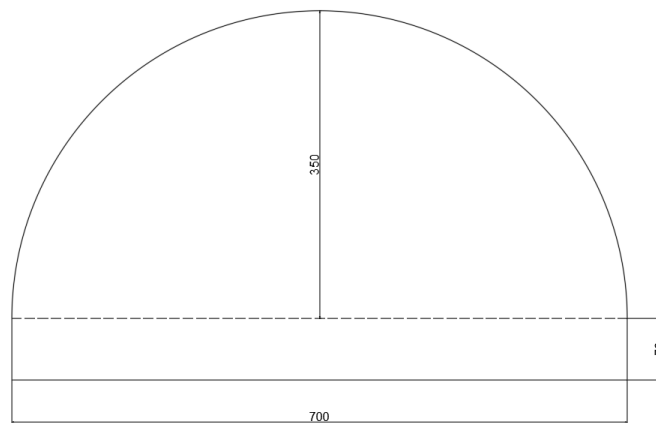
sección transversal de la cámara de aislamiento. Fuente Autor
